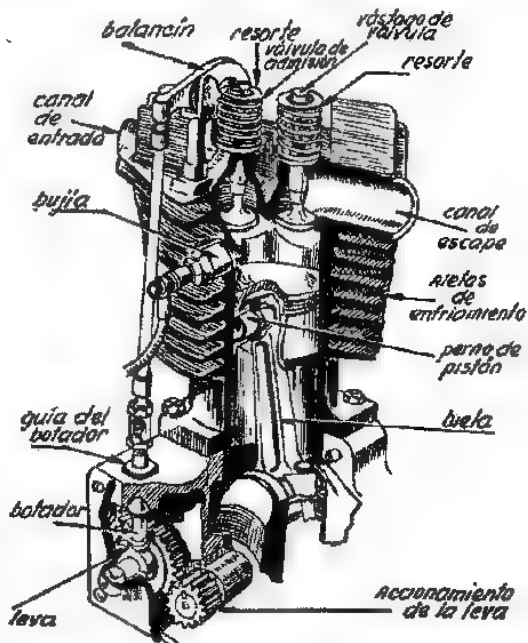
Corte de un motor monocilíndrico mostrando sus diversas partes
